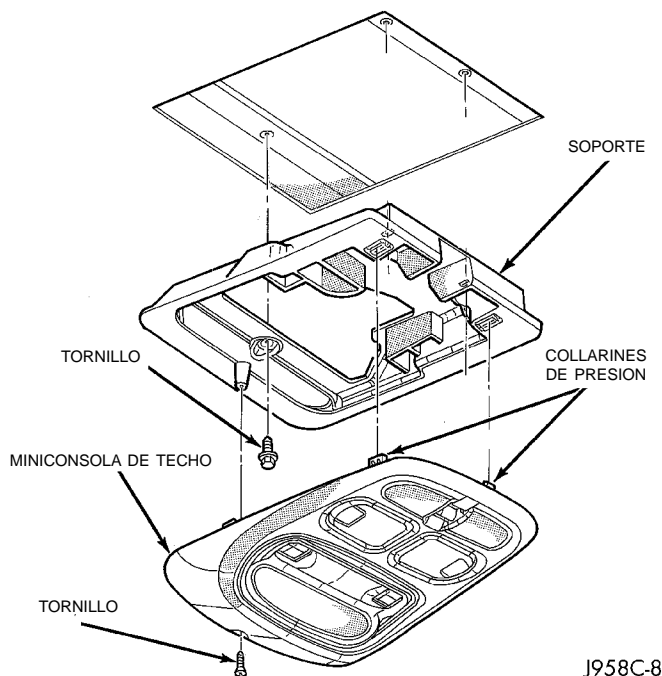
Desmontaje/instalación de la consola de techo - versión corta
